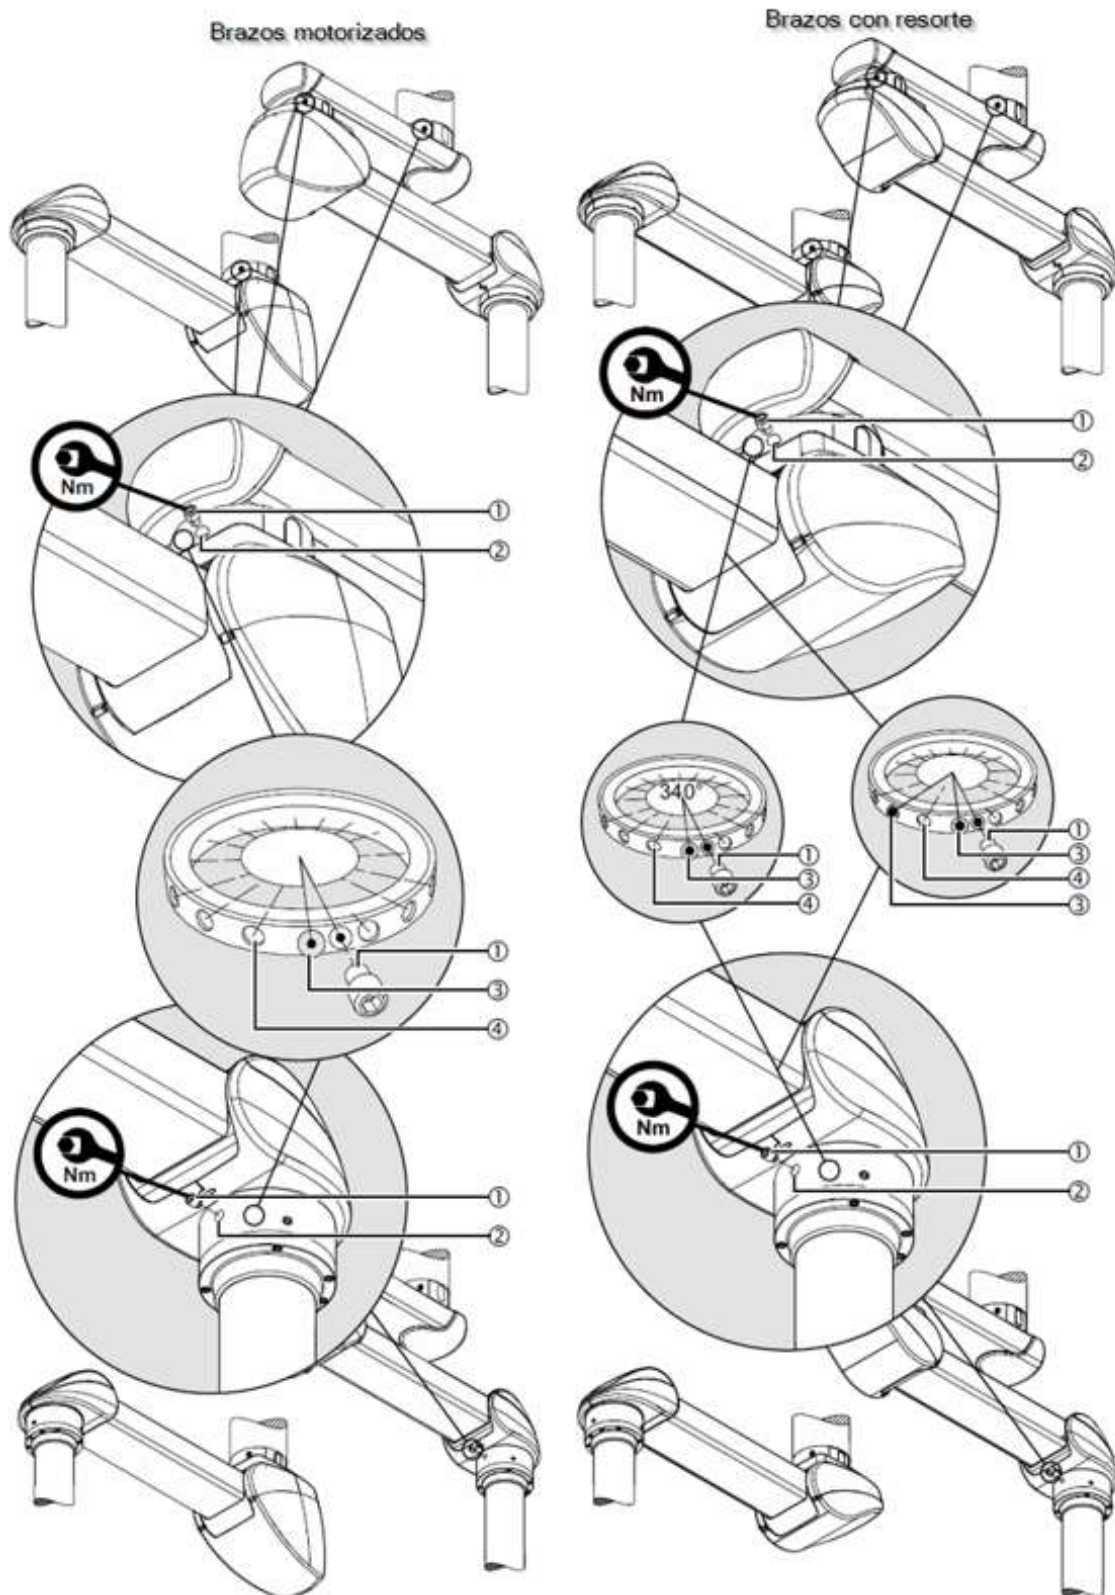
Afstelling van de draaibare aanslagen, niet-gemotoriseerde armen
